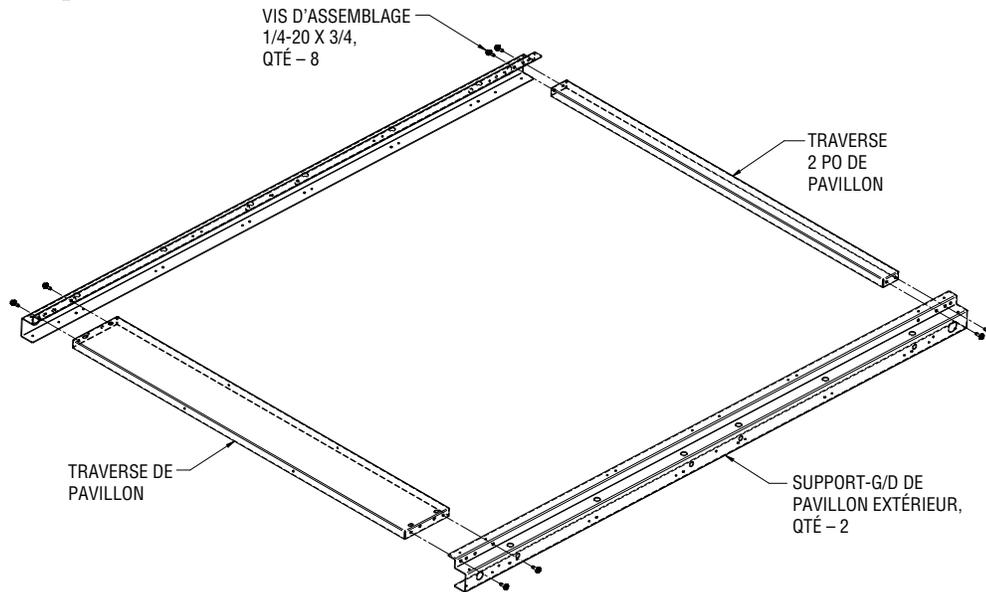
Vue en plongée de l'ensemble du cadre du pavillon
